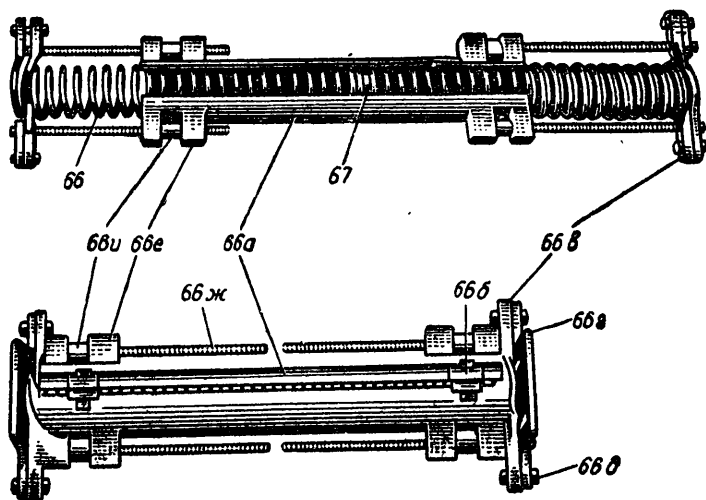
Приспособление для разборки и сборки амортизатора в минометах с неотъемными передними кронштейнами:
